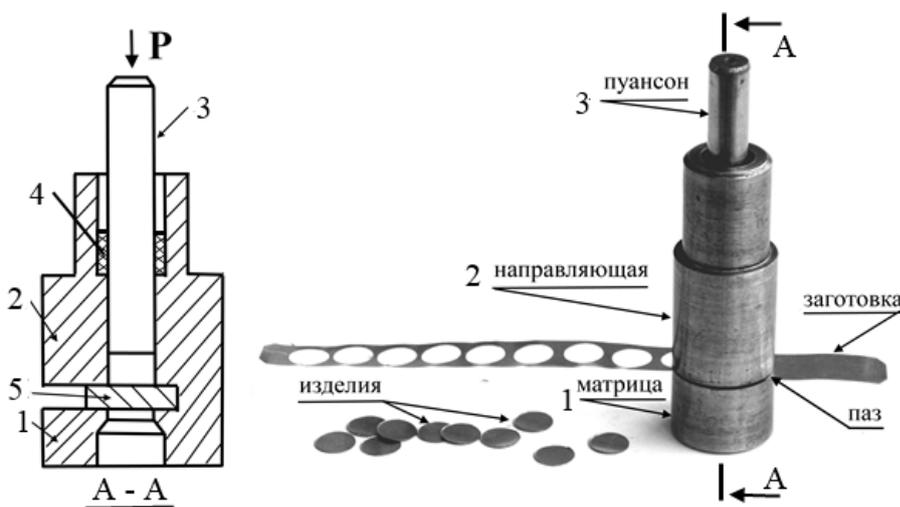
Конструкция и общий вид вырубного штампа
